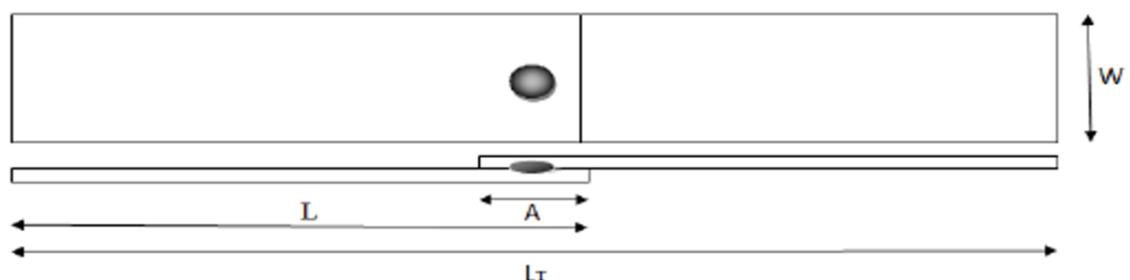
Dimensions des éprouvettes soudées ($L = 135$ mm ; $L_r = 240$ mm ; $W = 20$ mm ; $A = 30$ mm ; $E = 1,5$ mm)
